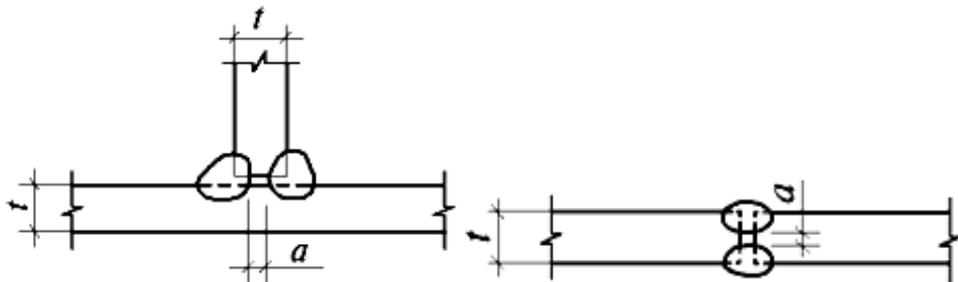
Непровар в корне шва при двусторонней сварке в угловых и стыковых соединениях
